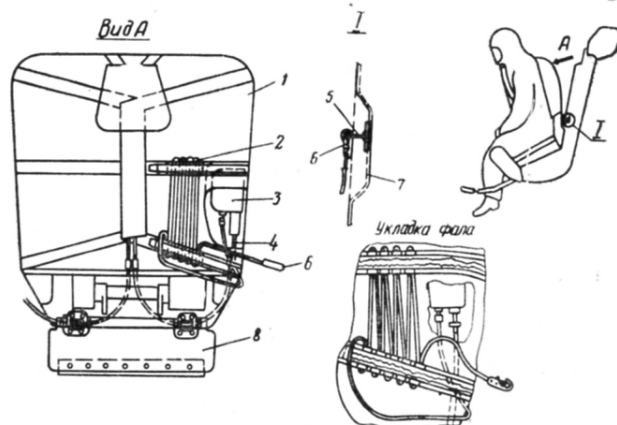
Спинка кресла и установка прибора ППК-У-405А: 1—ранец; 2—фал; 3—полуавтомат ППК-У-405А; 4—трос; 5—ушко; 6—карабин; 7—контейнер; 8—щиток
